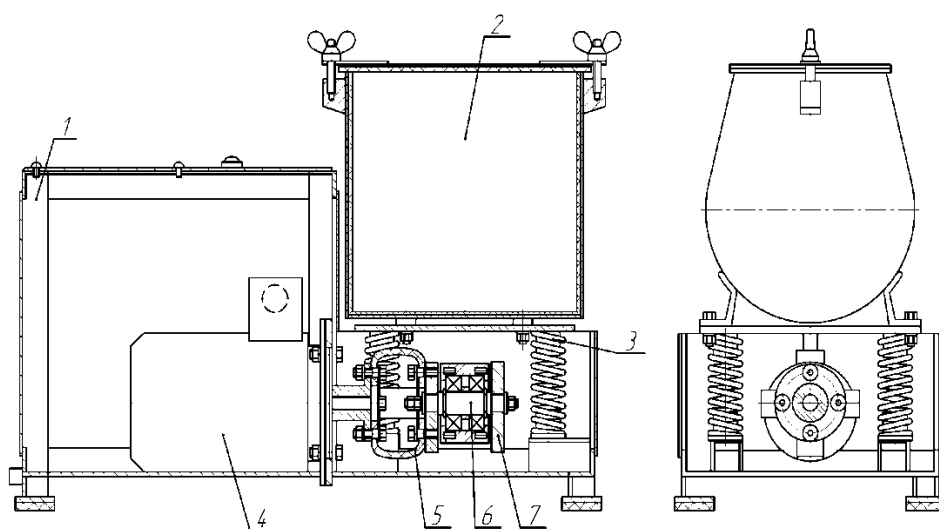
Конструкция виброгалтовочного станка с U-образным контейнером
